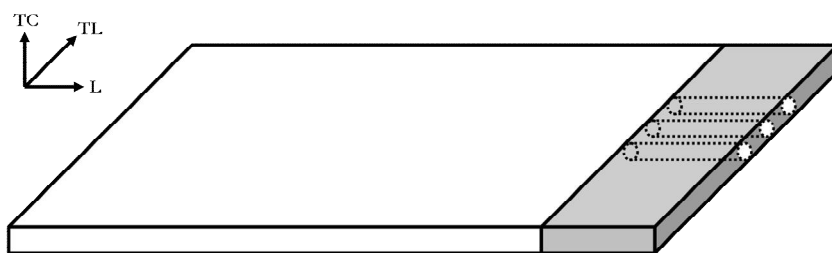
Plan de prélèvement des éprouvettes dans la tôle (L : Laminage, TL : Travers long, TC : Travers court).
